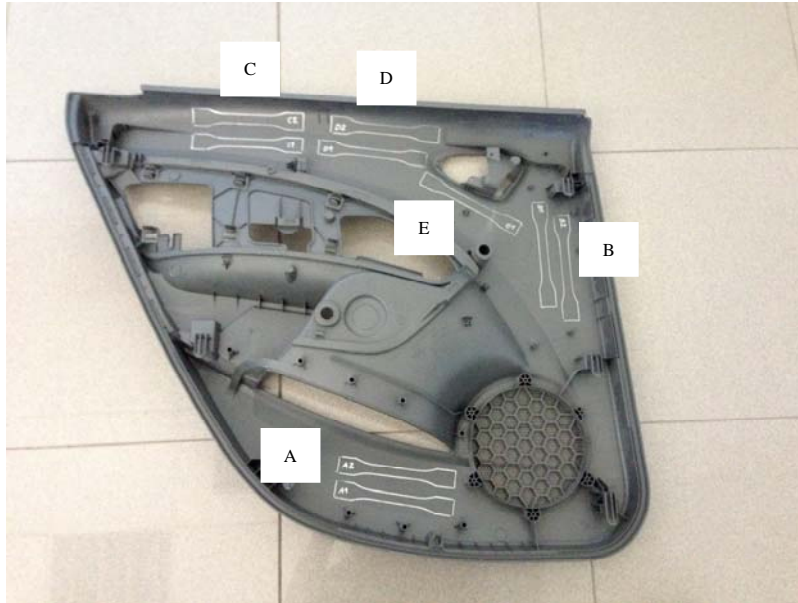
Zonas de extracción de planchas para ensayo. Panel Trasero
